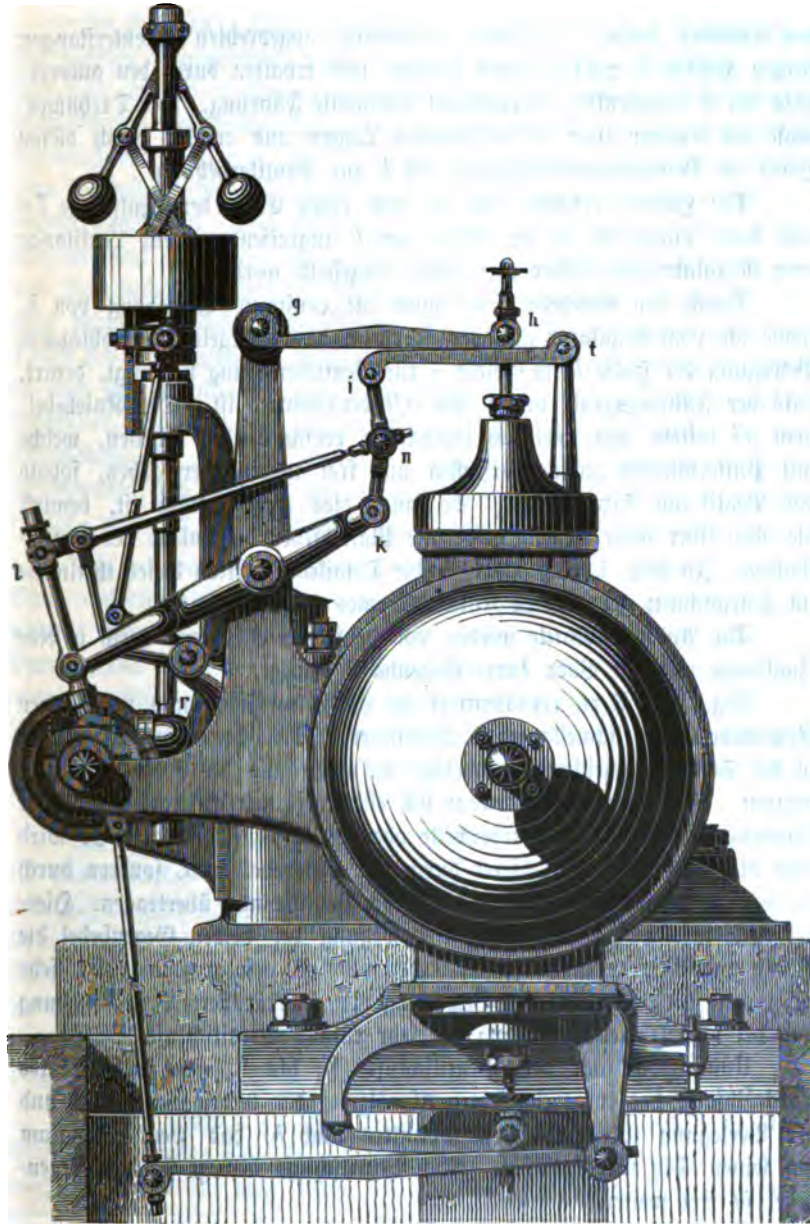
Tolkman-Steuerung mit Gegenhebeln.
